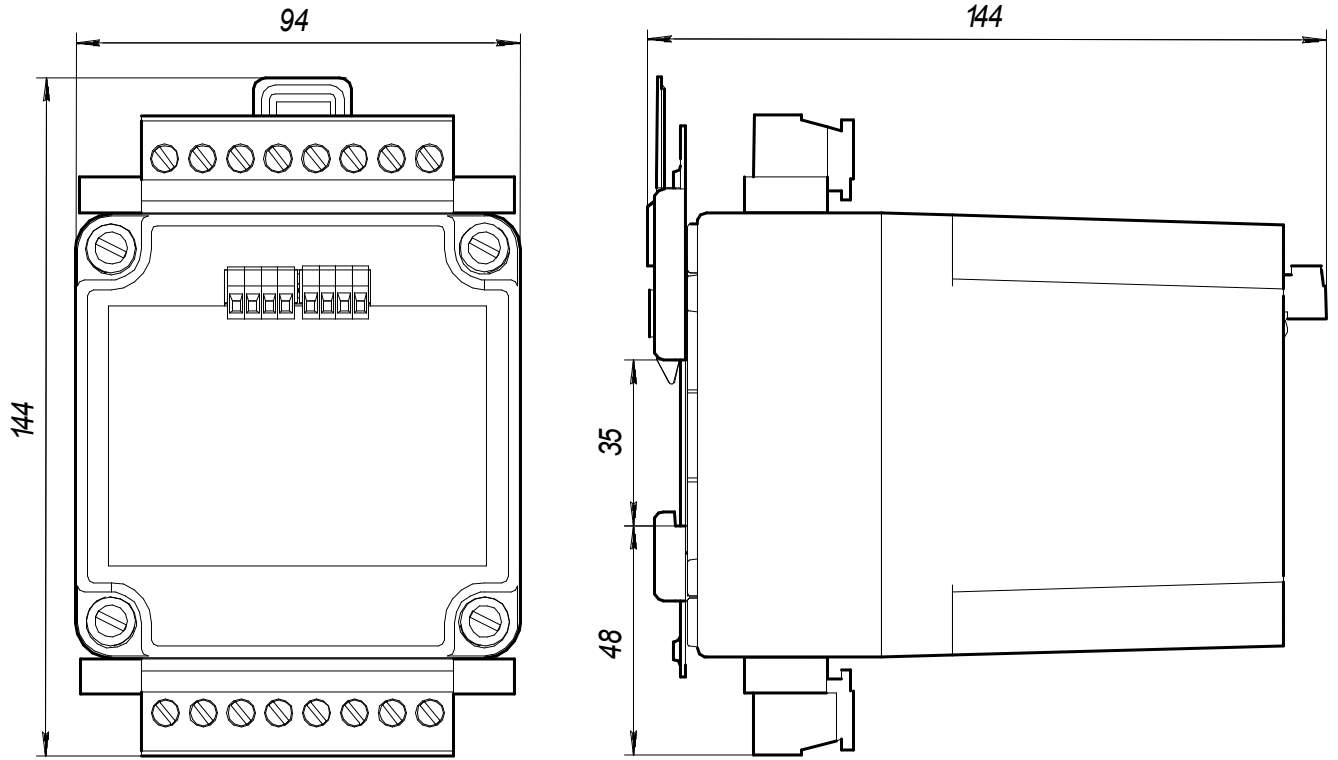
Габаритные и присоединительные размеры ПИ849Ц/XX-0 с креплением на DIN-рейку
